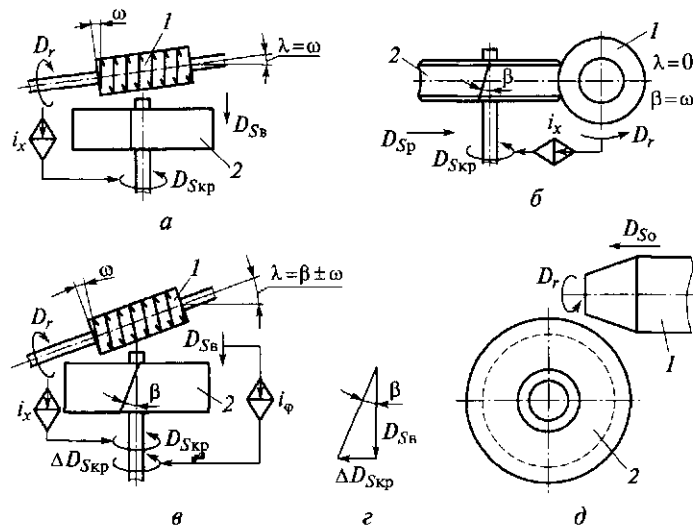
Принципиальные схемы нарезания прямозубого (а), червячного (б, д), косозубого (в) цилиндрических зубчатых колес червячно-модульной фрезой и схема формирования угла наклона зуба (г):
